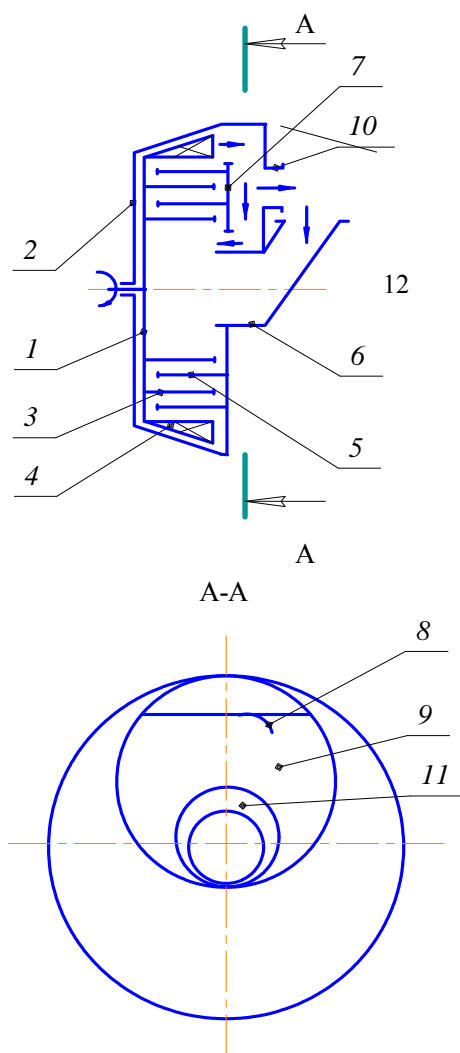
Дисмембратор с классифицирующей камерой: 1 – ротор; 2 – корпус; 3, 5 – измельчающие элементы; 4 – крыльчатка; 6 – крышка; 7 – стенка; 8, 11 – отверстия; 9 – классифицирующая камера; 10 – выгрузочный патрубок; 12 – загрузочный патрубок
